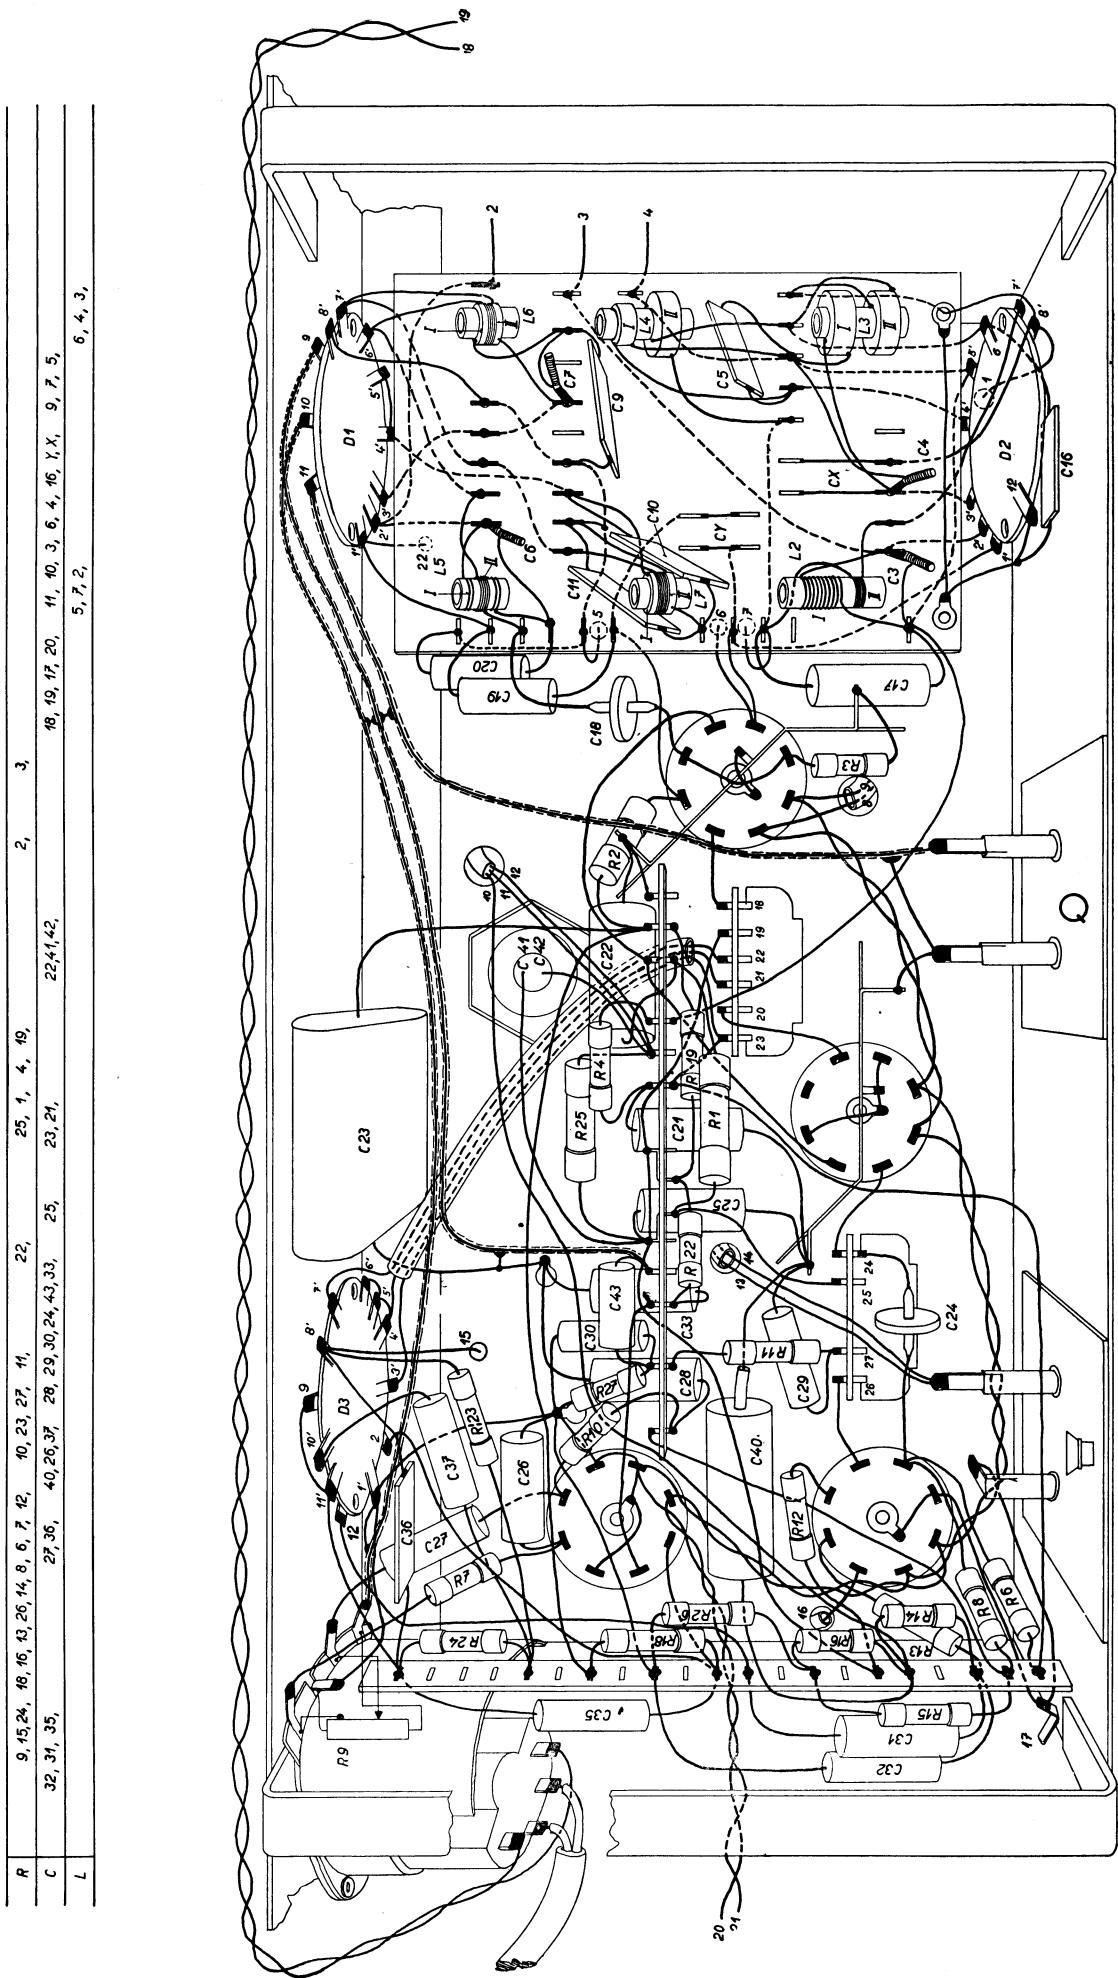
VYVAŽOVACÍ BODY NA CHASSIS
